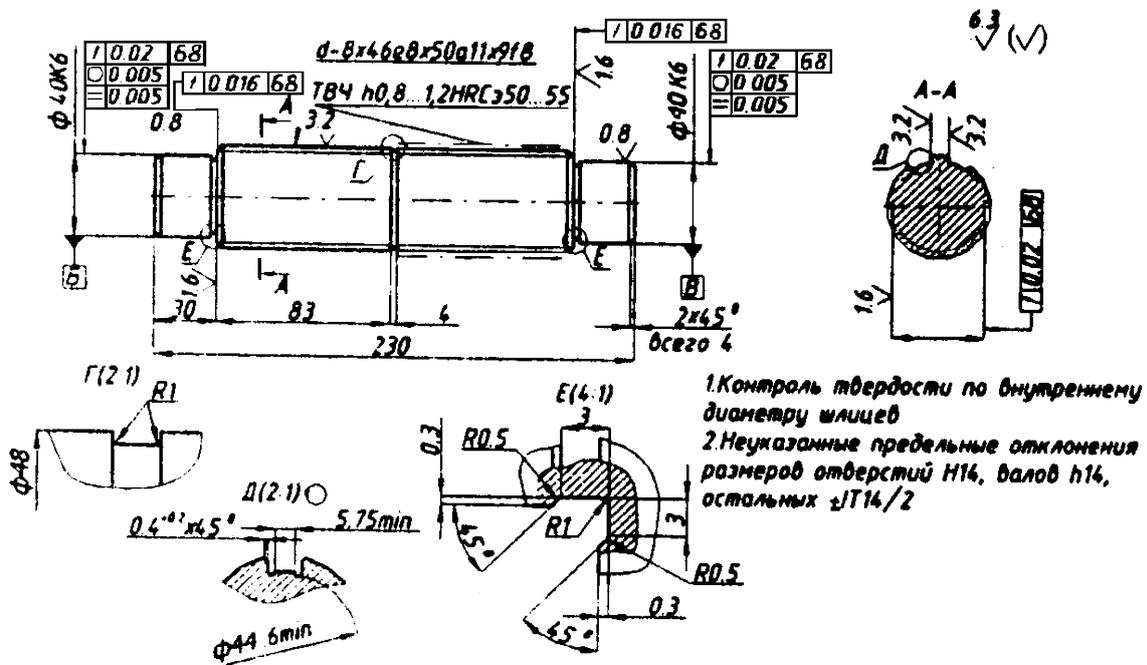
Шлицевый вал двусторонней ступенчатости.
